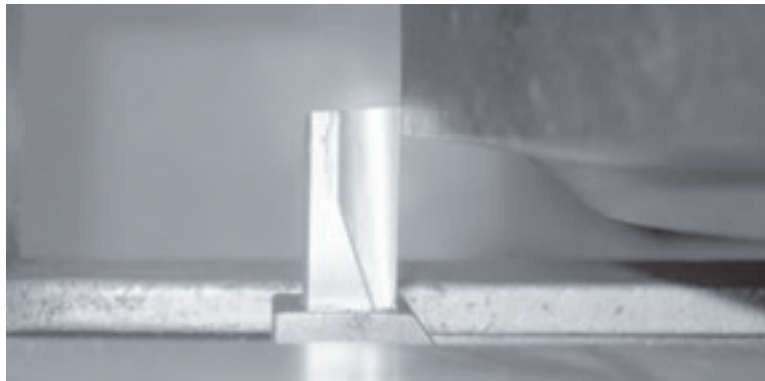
Posicione el buril de manera que toque el diámetro externo del tubo.
